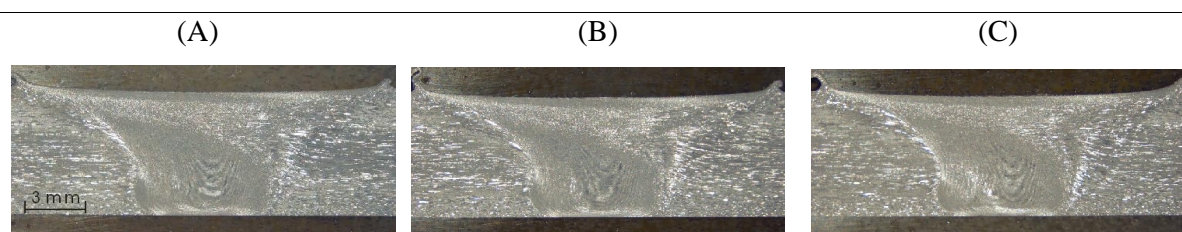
Amostras da seção transversal - ferramenta de soldagem facetada.
